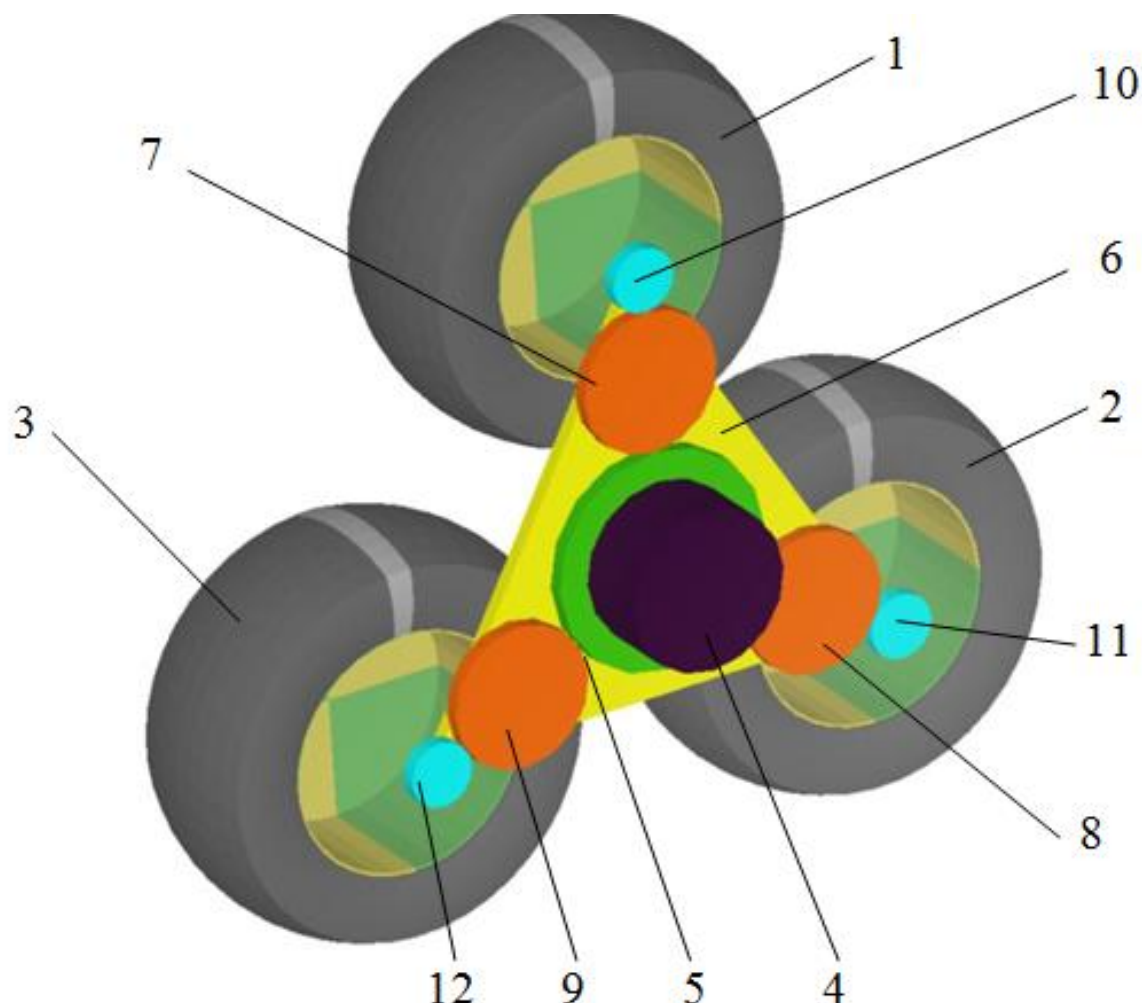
Схема колесно-шагающего трехкаткового движителя
